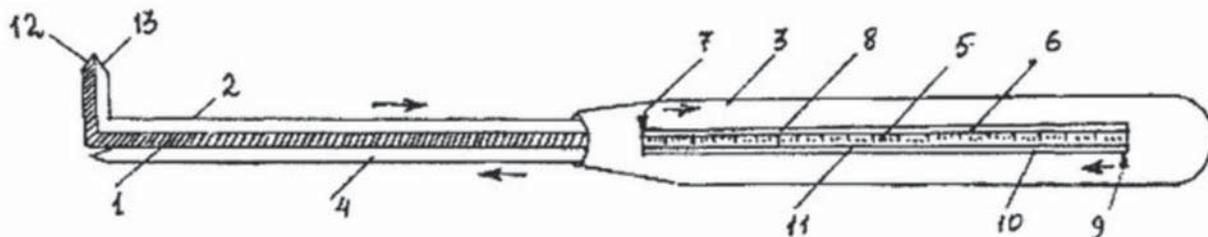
Схематическое изображение анатомического измерителя: 1 – неподвижный стержень; 2 – подвижный стержень; 3 – рукоятка; 4 – стержень глубиномера; 5 – шкалы; 6 – верхняя грань; 7 – рычаг подвижного стержня; 8 – паз для рычага подвижного стержня; 9 – рычаг глубиномера; 10 – паз для глубиномера; 11 – нижняя грань шкалы; 12 – неподвижный отметчик; 13 – подвижный отметчик.
